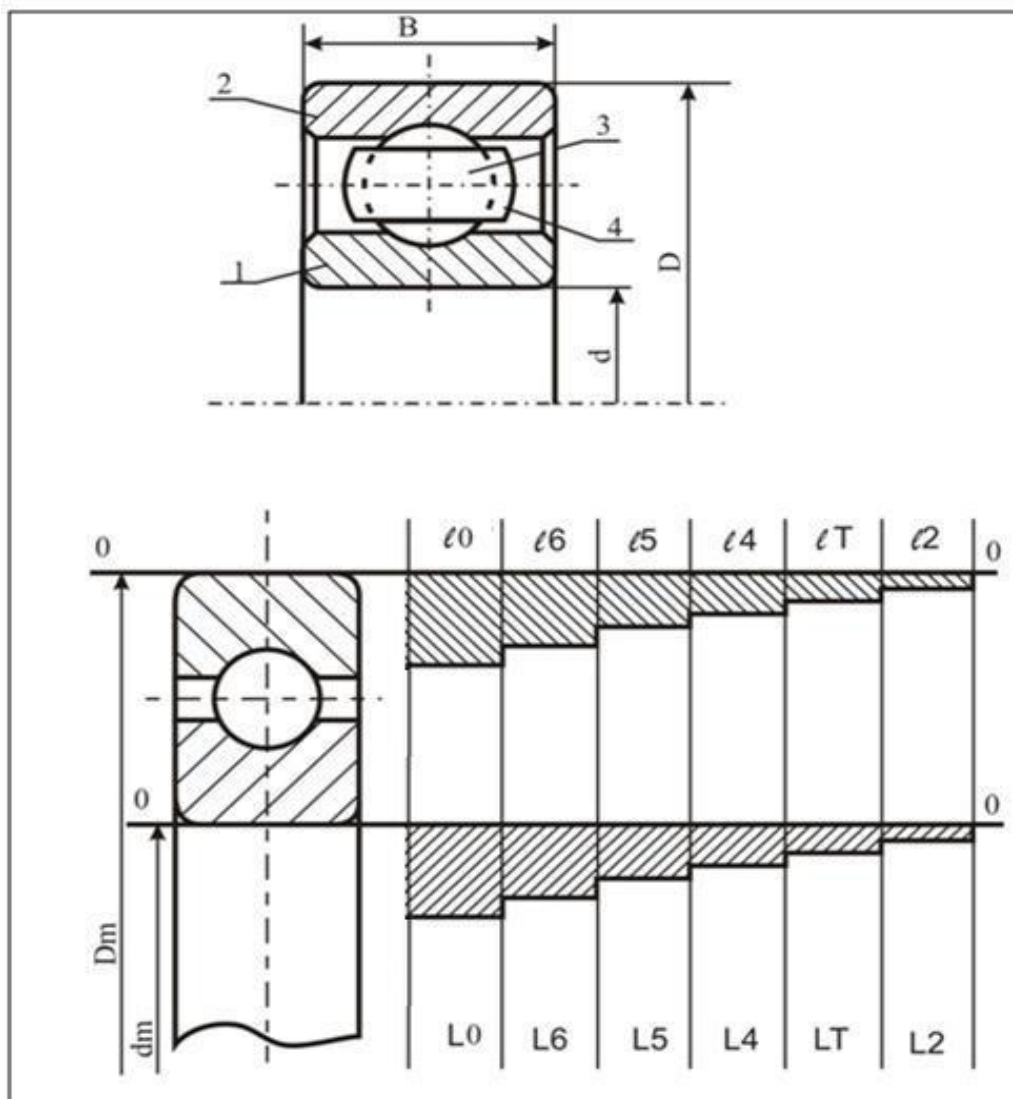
Шариковый однорядный подшипник качения: а – конструктивные элементы; б – схемы расположения полей допусков по классам точности на средний наружный диаметр наружного кольца и средний внутренний диаметр внутреннего кольца для шариковых радиальных подшипников качения
